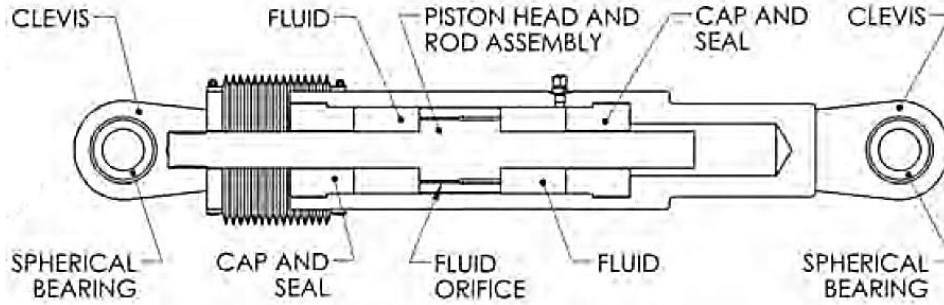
Corte longitudinal de dispositivo con vástago de pistón pasante.
